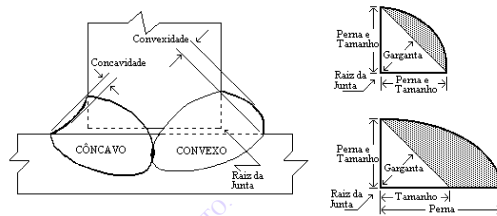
(b) - Geometria do Cordão de Solda de Junta em Ângulo (Filete).
